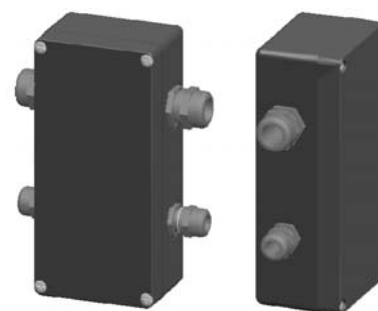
Соединительный корпус FG30-20 Ex-II
